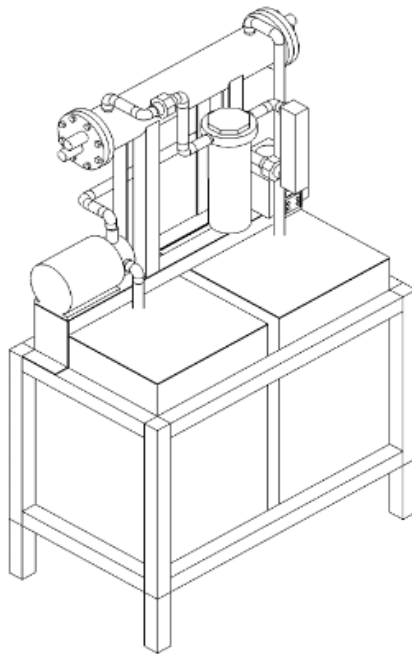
Technical Drawing Assembly Prototipe Tampak Belakang
